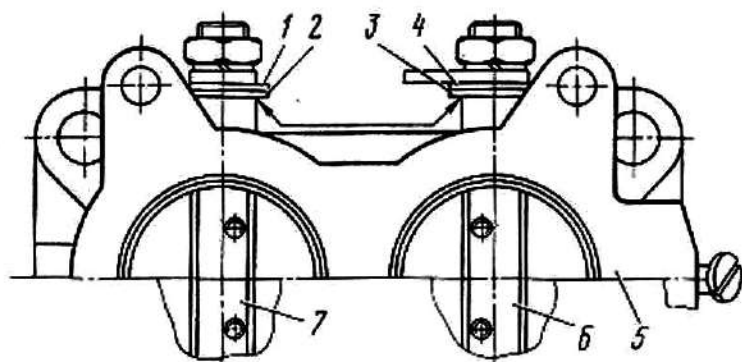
Регулировка зазора между рычагами осей дроссельных заслонок и бобышками корпуса:
